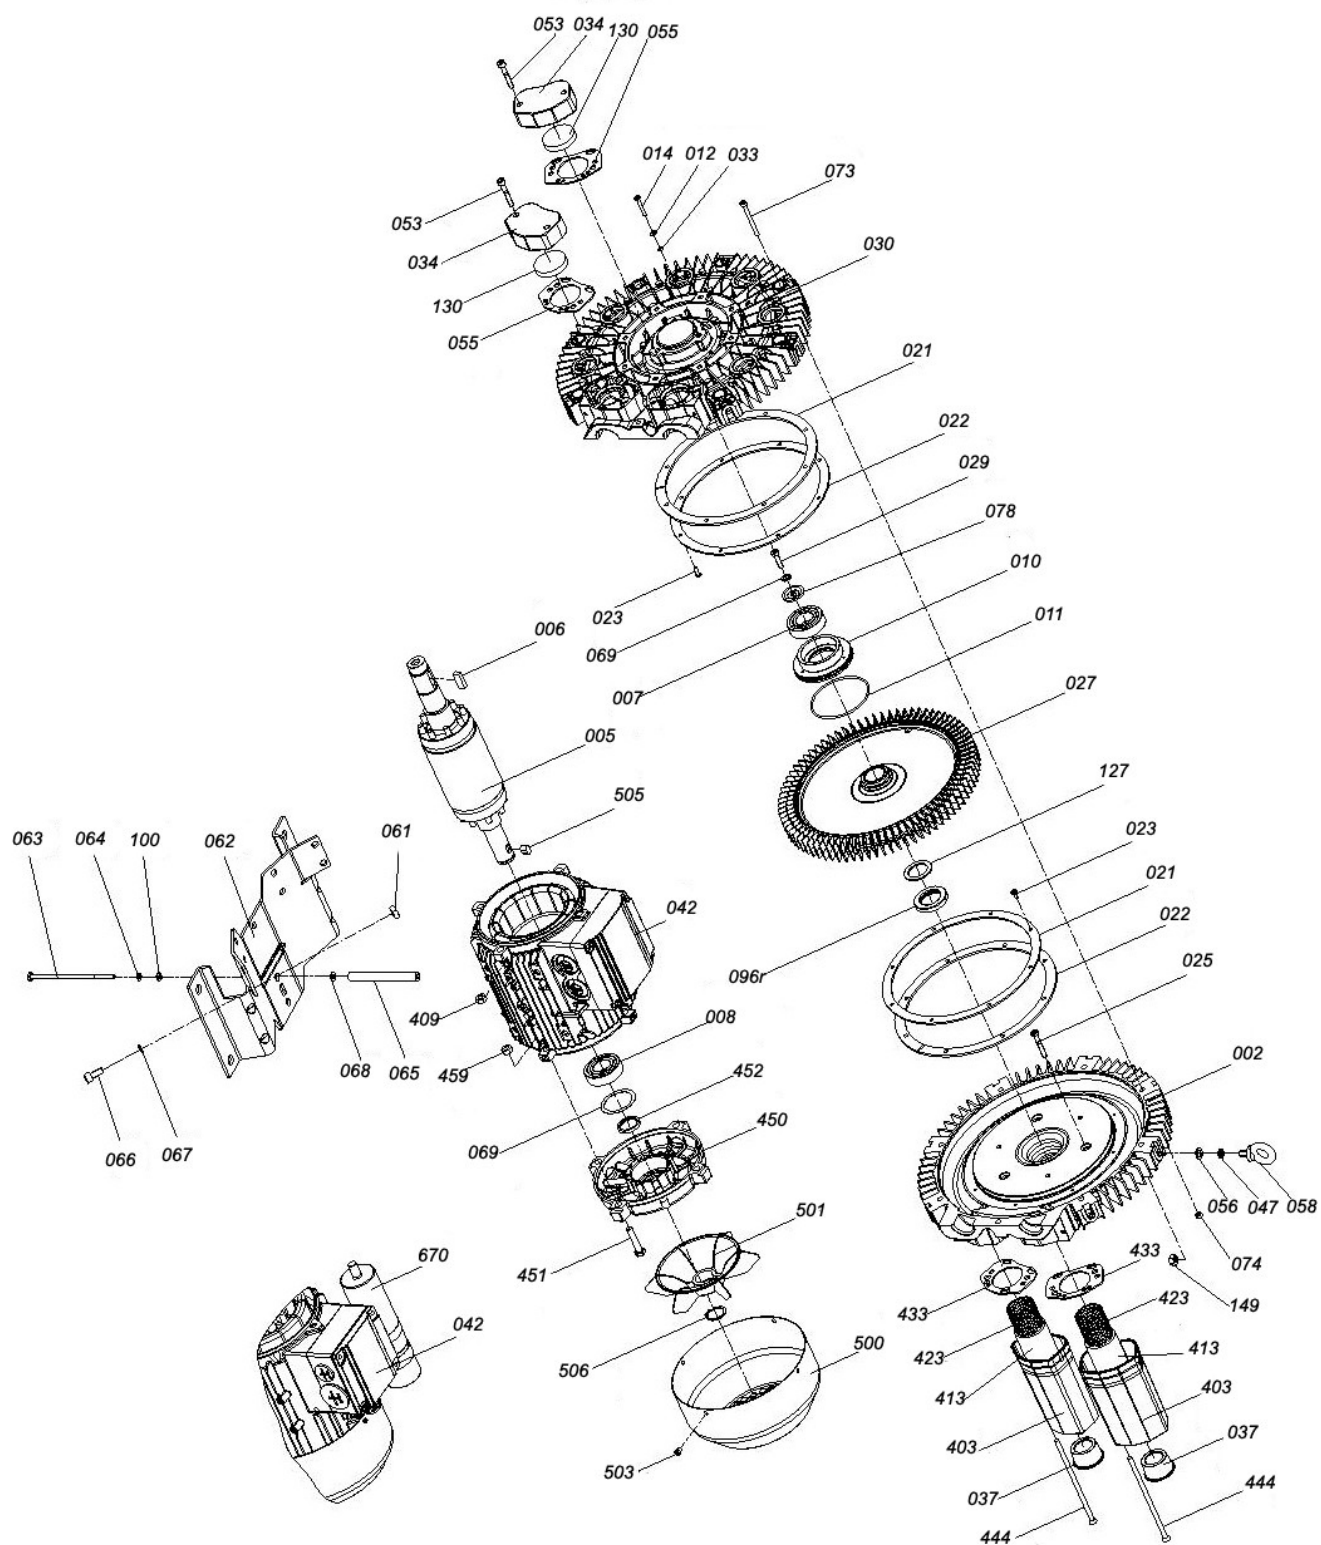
Деталировка одноступенчатых воздуховок 4RB
